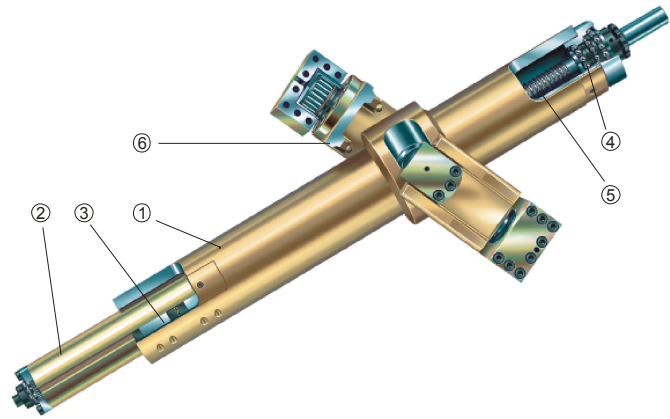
Телескопічна штанга змінної довжини: 1 – зовнішня труба; 2 – внутрішня труба; 3 – лінійні напрямні; 4 – упорний підшипник; 5 – гвинтова передача; 6 – карданний шарнір
